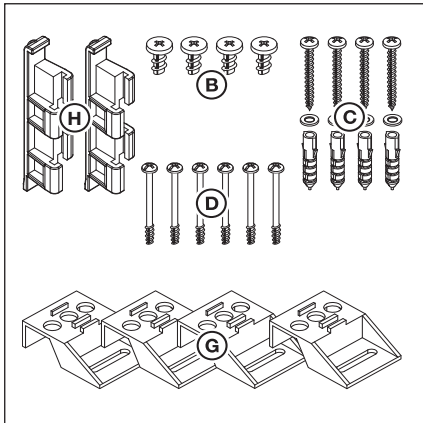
Содержимое пакета с принадлежностями для дополнительного корпуса
